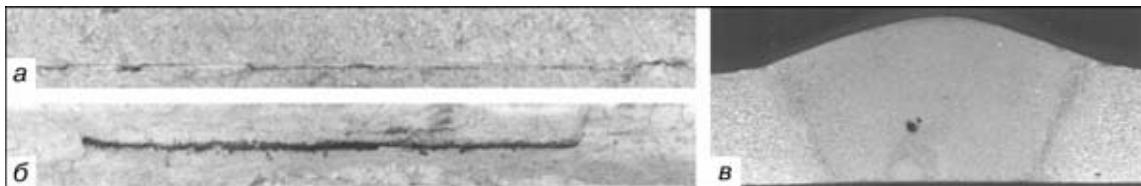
Протяженные нитевидные включения оксидной плены в изломах швов (*a*, *b*) и на поперечном макрошлифе (*c*), образующиеся при аргонодуговой сварке литийсодержащих алюминиевых сплавов с неплавящимся электродом
